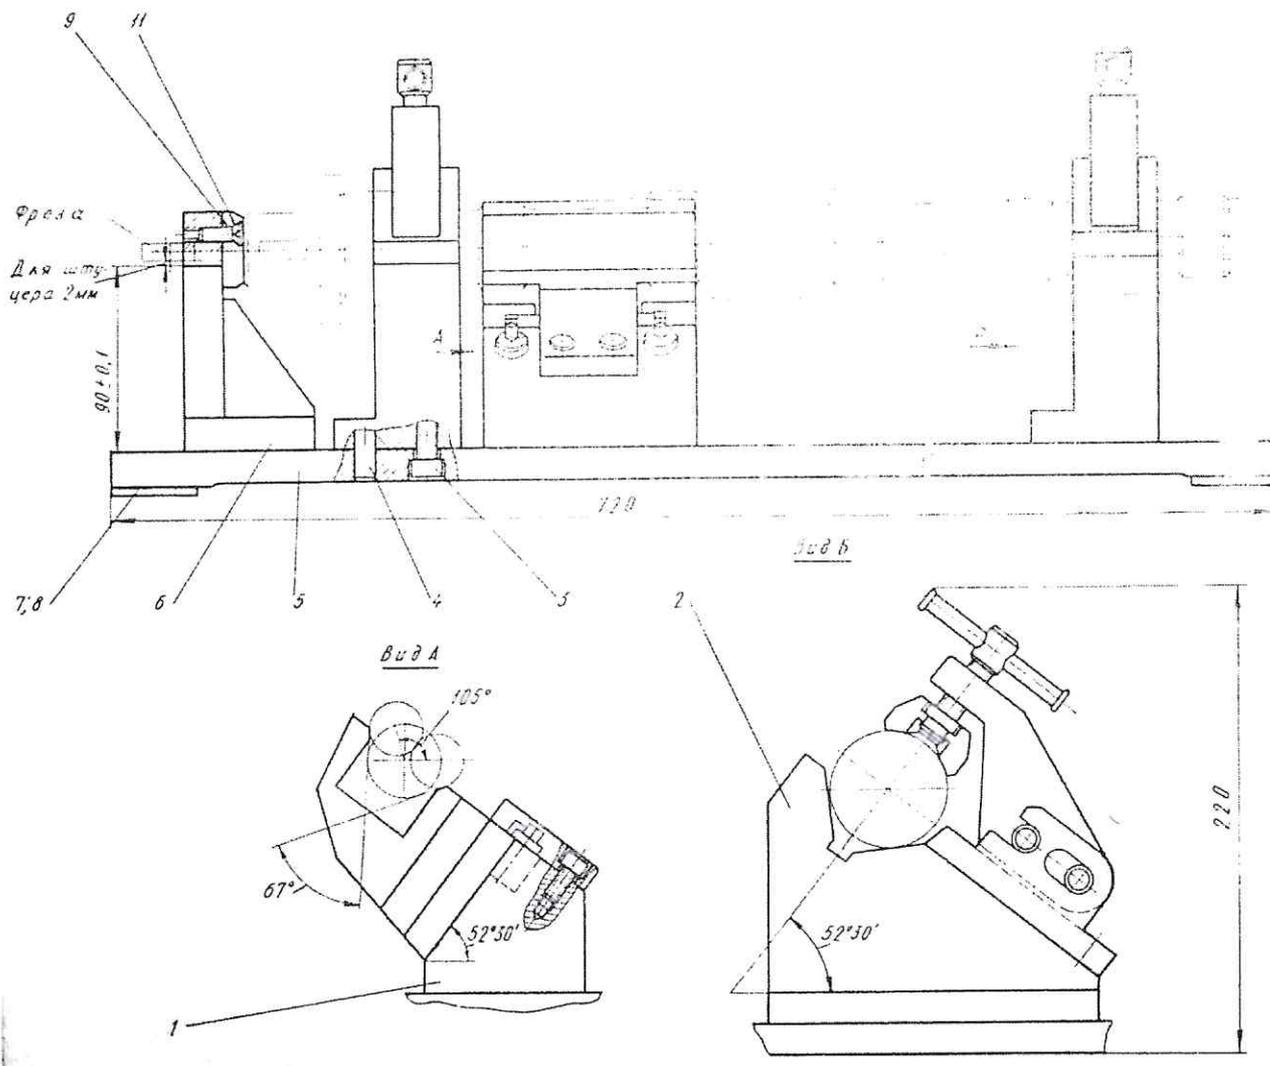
Приспособление для фрезерования шпоночных пазов на распредвалах 70-7215-1510 ГОСНИТИ.
